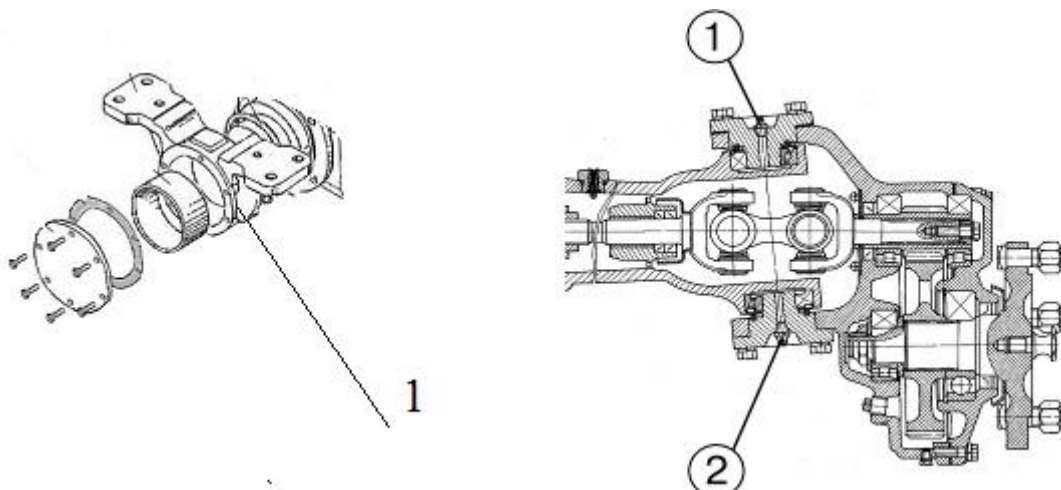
Смазка подшипников шкворней колесных редукторов ПВМ и
